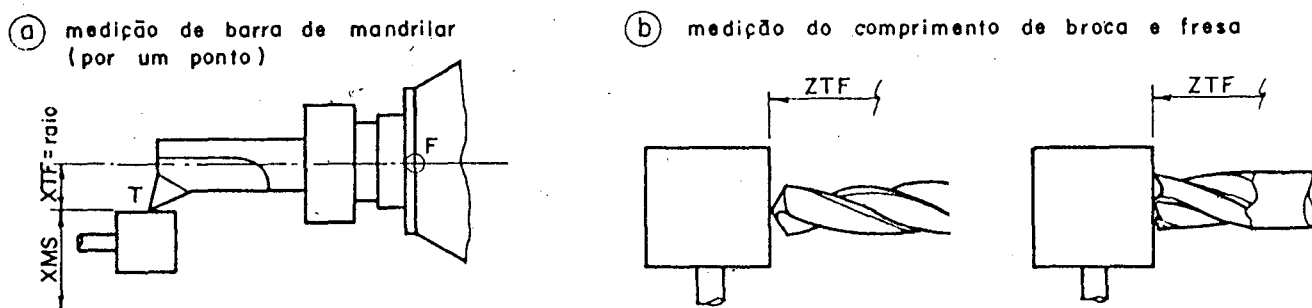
Medição de ferramentas rotativas em furadeiras, fresadoras e centros de usinagem
